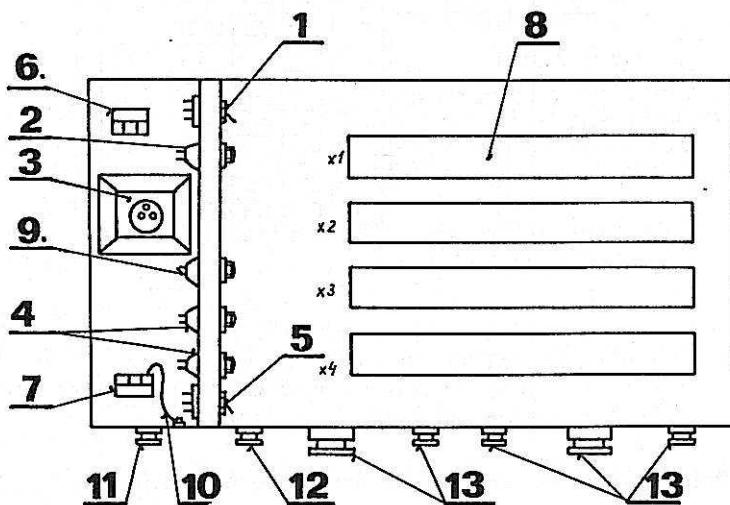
Připojení zemnící spojky k víku skříně
